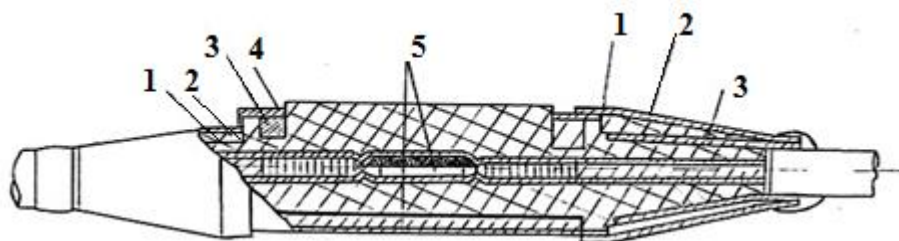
,б. Соединительная муфта для кабелей напряжением 35 кВ: 1 – экран конуса; 2 – конус; 3 – корпус; 4 – экран корпуса; 5 – место соединения
